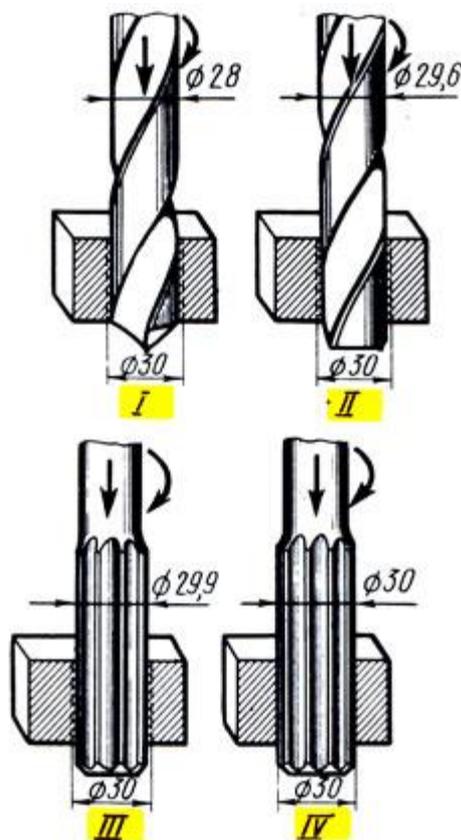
Последовательность обработки отверстия: I - сверление, II - зенкерование, III - черновое развертывание, IV - чистовое развертывание
